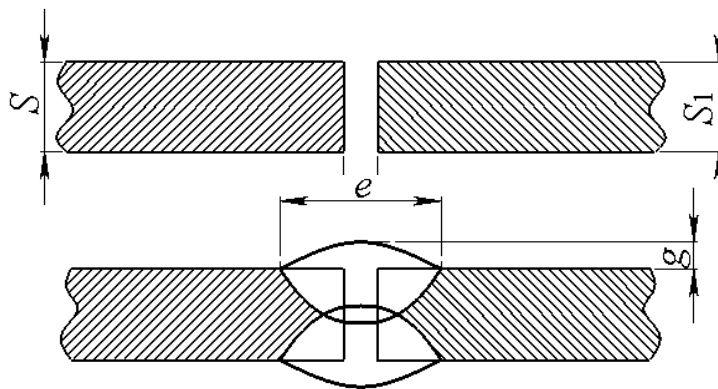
Стыковой сварной шов ГОСТ 5264–80–С7
